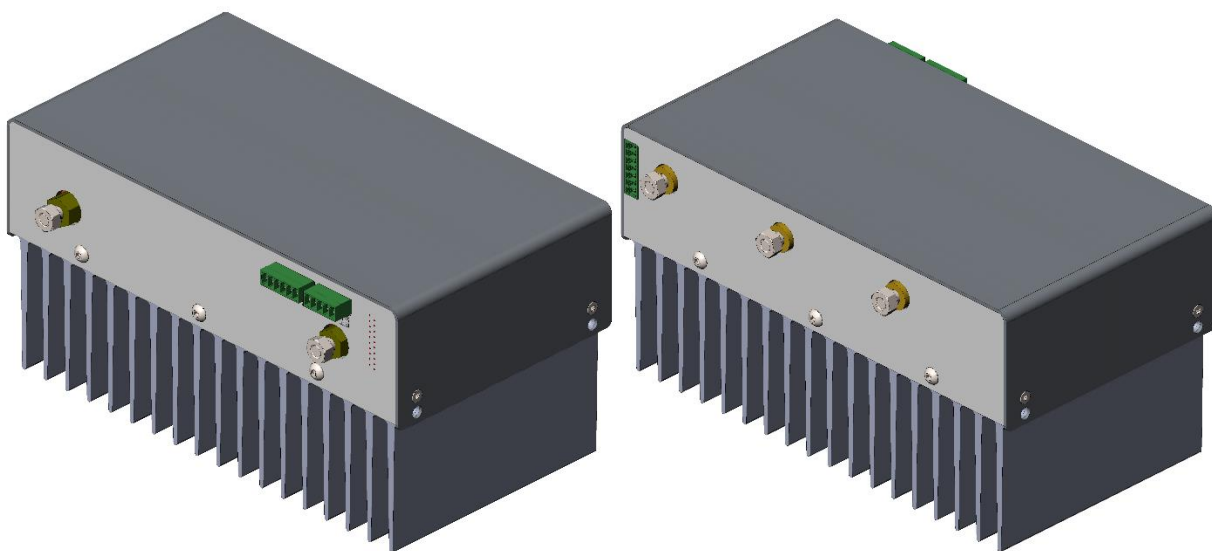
Внешний вид инвертора КЛИ 150-6
